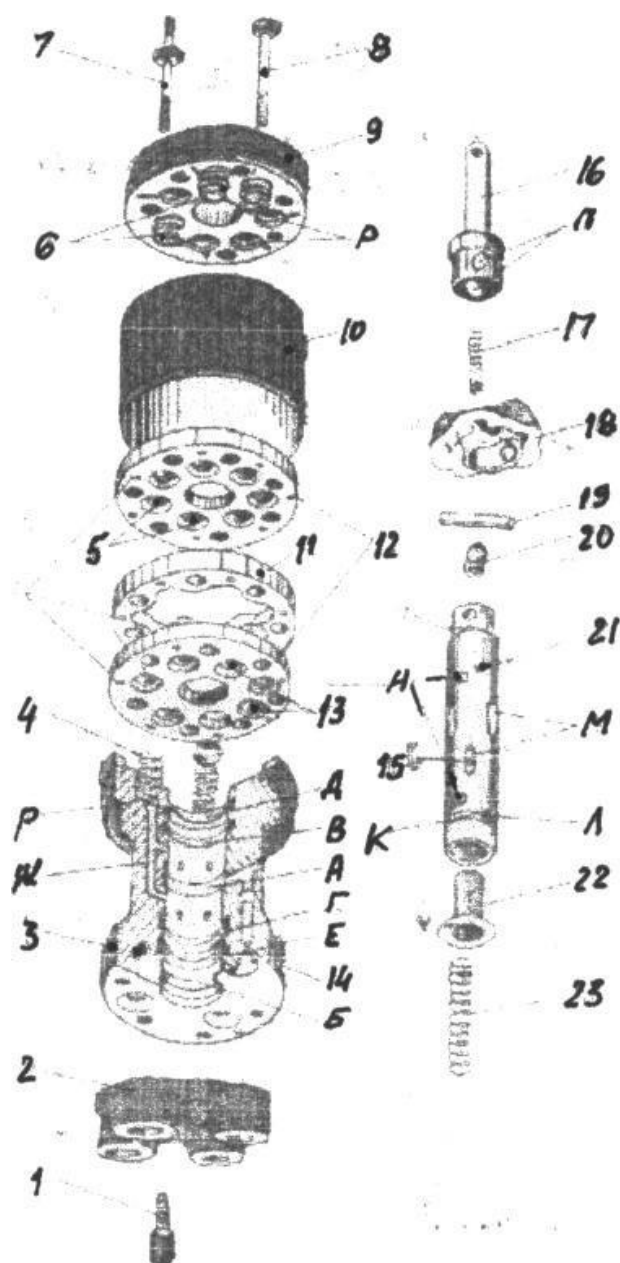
Насос - дозатор НД-80: 1 и 8 - болт; 2 - нижняя крышка; 3 - корпус; 4, 6, 17 и 23 - пружина; 5 и 13 - шарик; 7 - шпилька; 9 - верхняя крышка; 10 - бандажное кольцо; 11 - промежуточное кольцо; 12 - обойма цилиндров; 14 - обратный клапан; 15 - шариковый клапан; 16 - приводной вал; 18 - кулачковая дорожка; 19 - палец; 20 - втулка; 21 - золотник; 22 - колпачок; А и Б - кольцевая проточка для нагнетания; В и Г - кольцевая проточка для управления; Д и Е - кольцевая проточка для слива; Ж - Ф - образный канал; И - отверстия, соединяющие пружинные полосы корпуса и верхней крышки; К - кольцевая проточка; Л - радиальное несквозное отверстие; М - пазы овальной формы; Н - лыски; О - отверстие, связывающее внутреннюю полость золотника с полостью кулачковой дорожки; П - наклонные пазы; Р — пружинные полости корпуса и верхней крышки.
